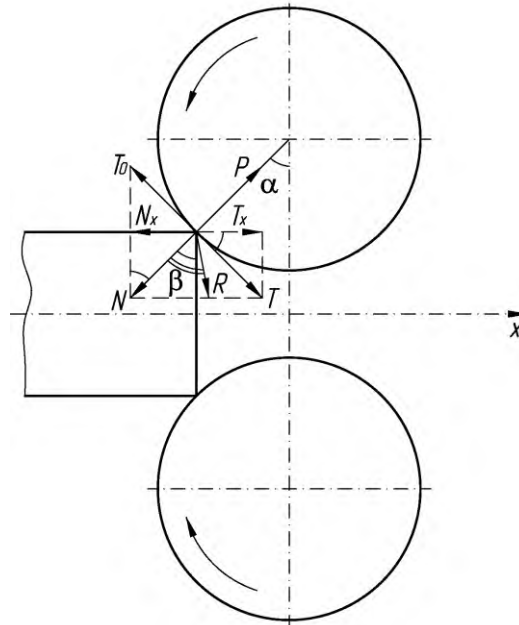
Схема захвата металла валками для неустановившегося периода прокатки
